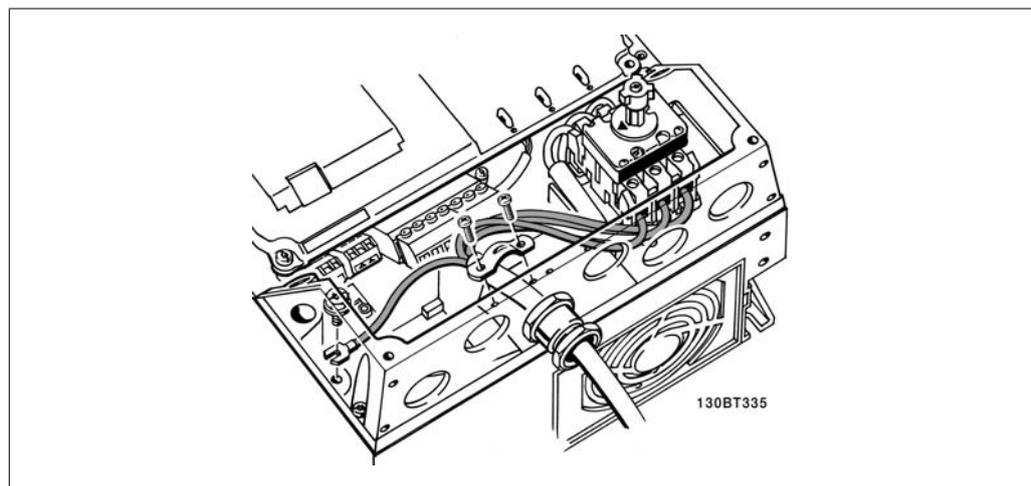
Connexion au secteur et à la terre avec sectionneur secteur.
